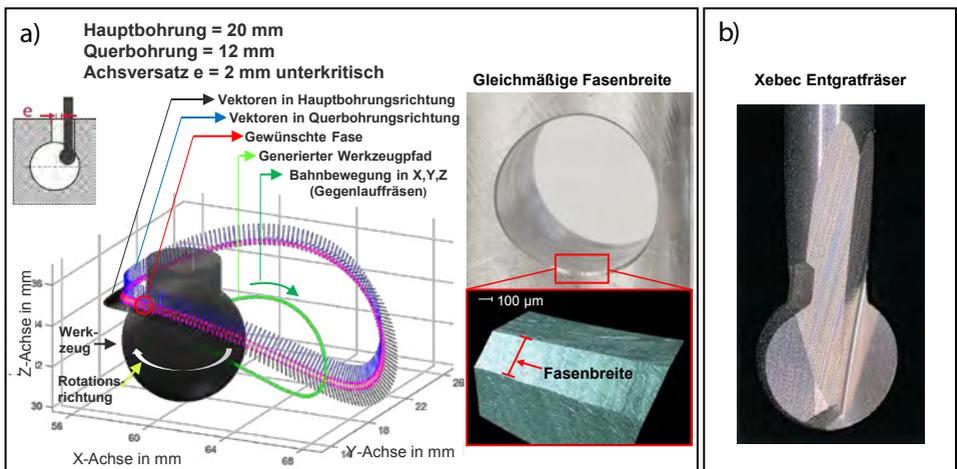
a) Werkzeugbahnsimulation für Kreuzbohrung mit 20 auf 12 mm b) Kugelkopf-Entgratfräser von Xebec, (Quelle: PTW TU Darmstadt)
